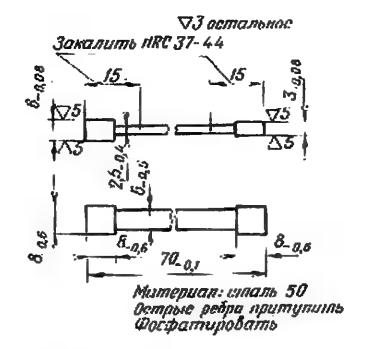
Плаблон для проверки спуска курка с боевого взвода
